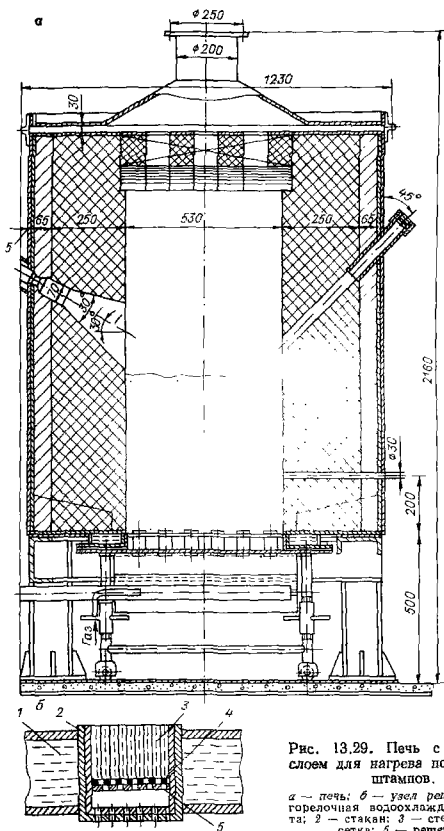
Печь с кипящим слоем для нагрева поверхности штампов.
